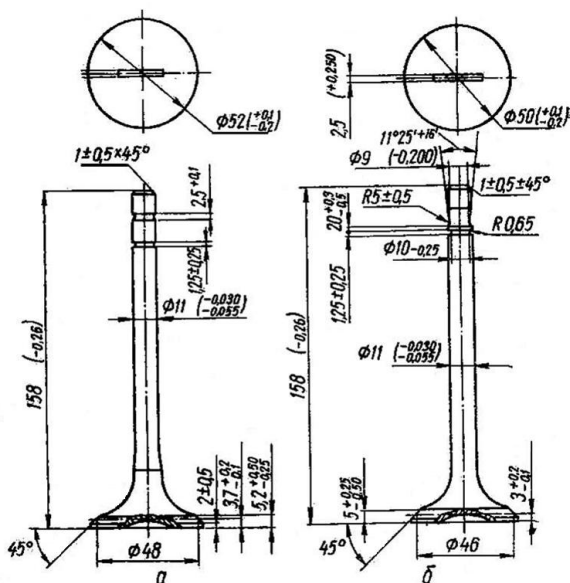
Детали для проведения измерений диаметра изготовления и отклонения формы расположения: впускные клапаны двигателей СМД-14 (деталь № СМД14-0604, а) и двигателей СМД-7 (деталь № СМД 1-0604, б).
